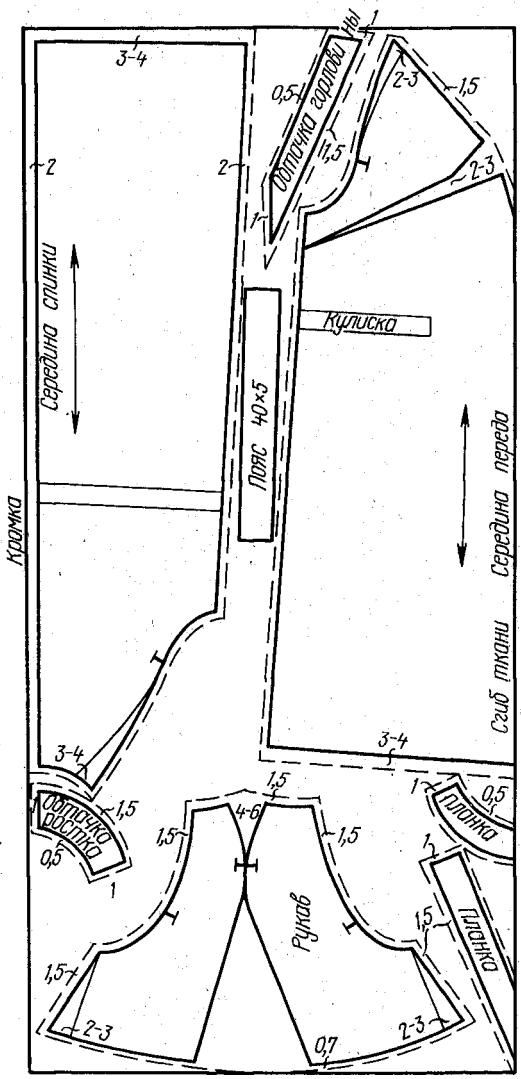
Раскладка выкроек на ткани и раскрой платья с отделочными планками
